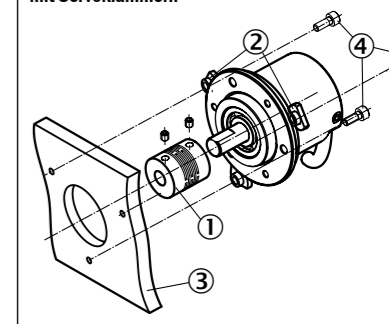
Anbau DBS50 Klemmflansch mit Servoklammern
